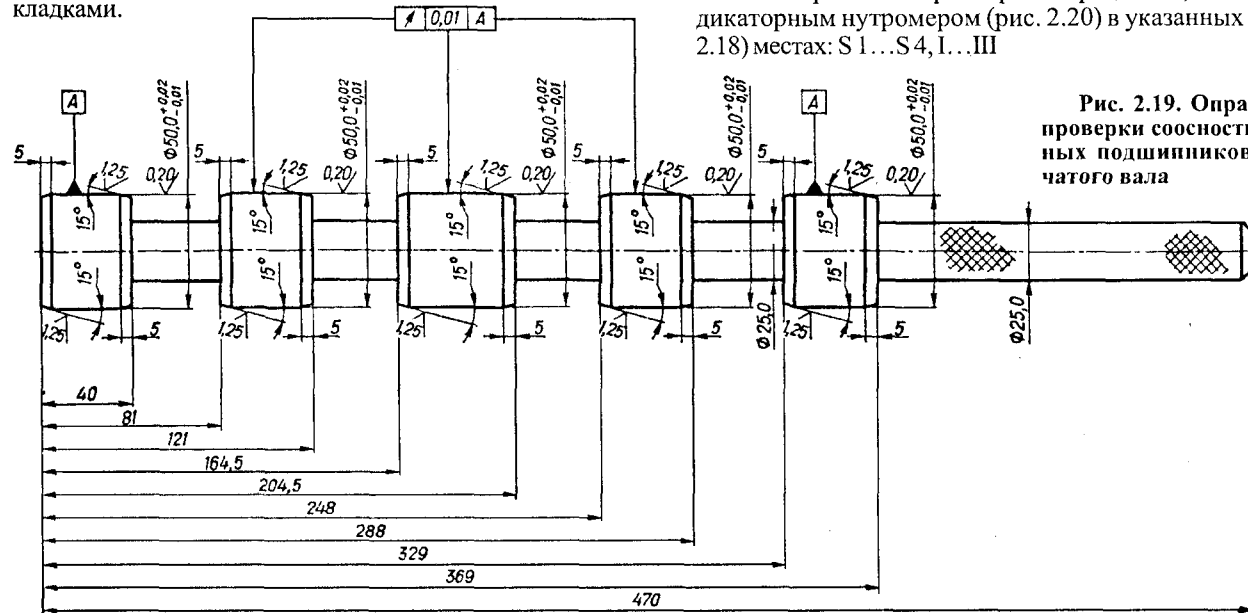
Оправка для проверки соосности коренных подшипников коленчатого вала
